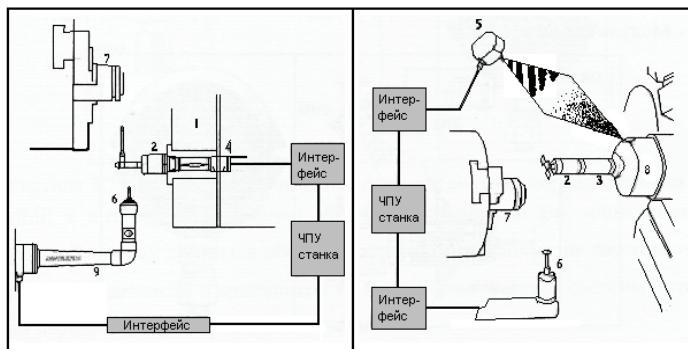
Применение контактных датчиков на токарных станках: 1 - револьверная головка токарного станка; 2 - контактный датчик; 3 - удлинитель; 4 - модули системы индуктивной передачи данных; 5 - оптический приемник; 6 - датчик наладки инструмента; 7 - обрабатываемая деталь; 8 - оптический передатчик
